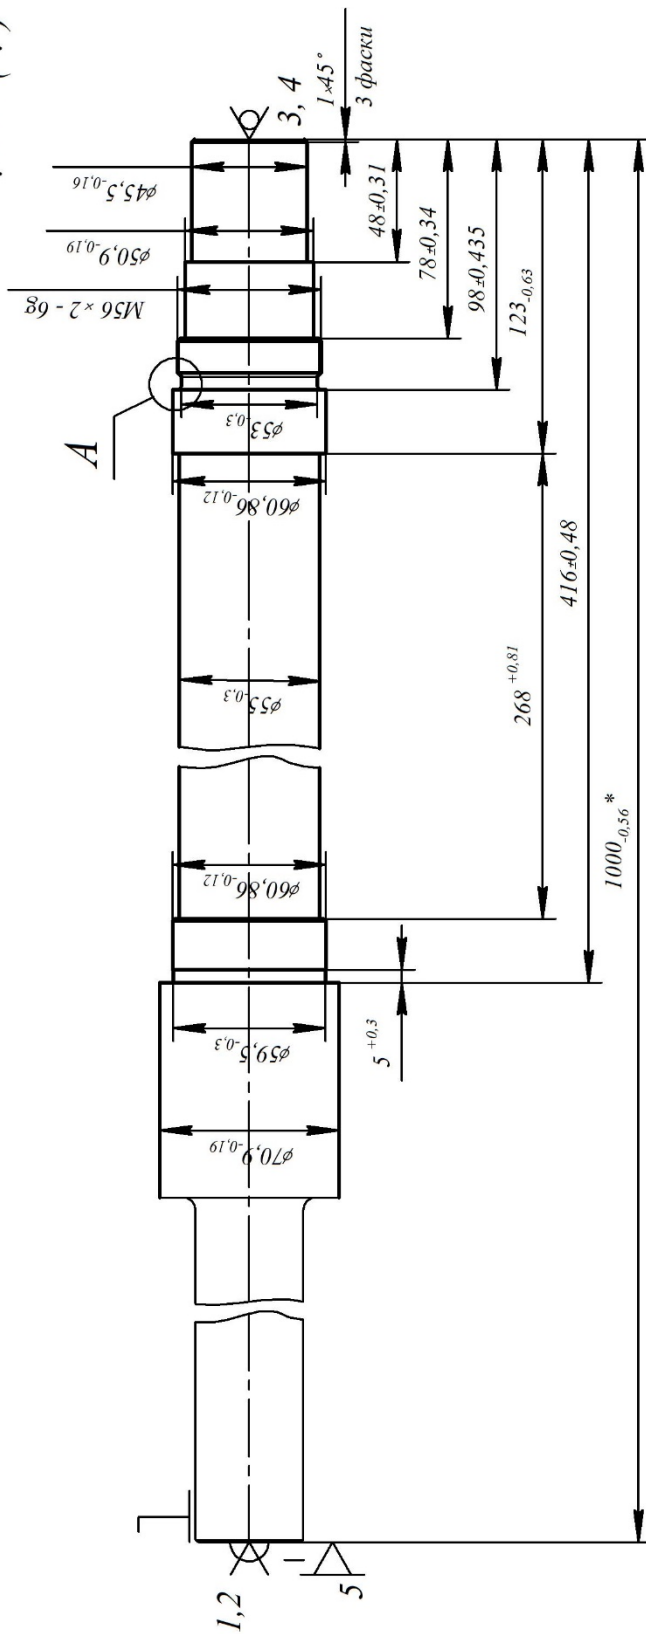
Схема базування заготовки на операції токарній 025, установ А
